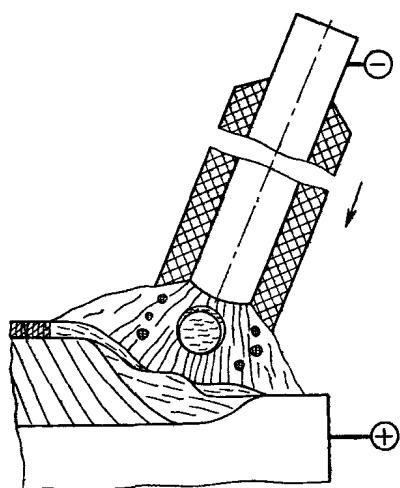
Схема подключения источника сварочного тока при прямой полярности
